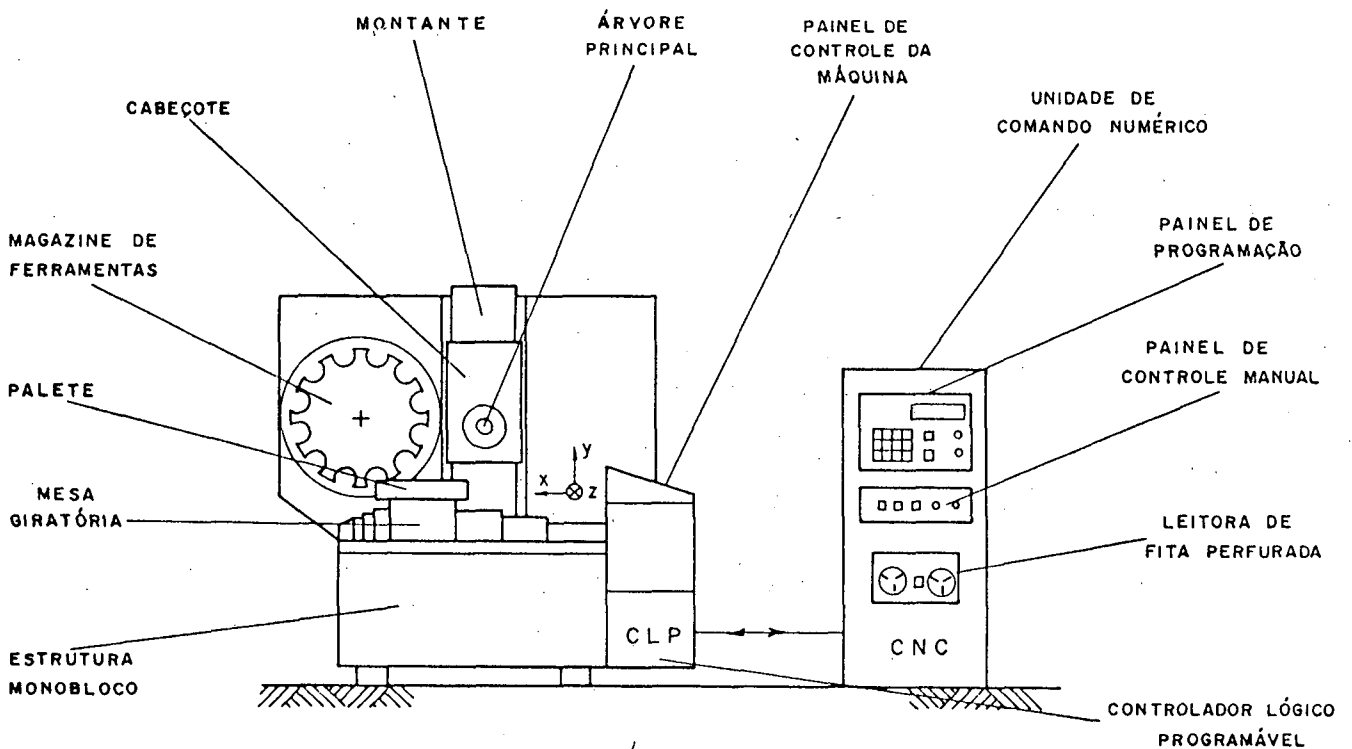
Centro de usinagem com CNC utilizado para o SMCP
